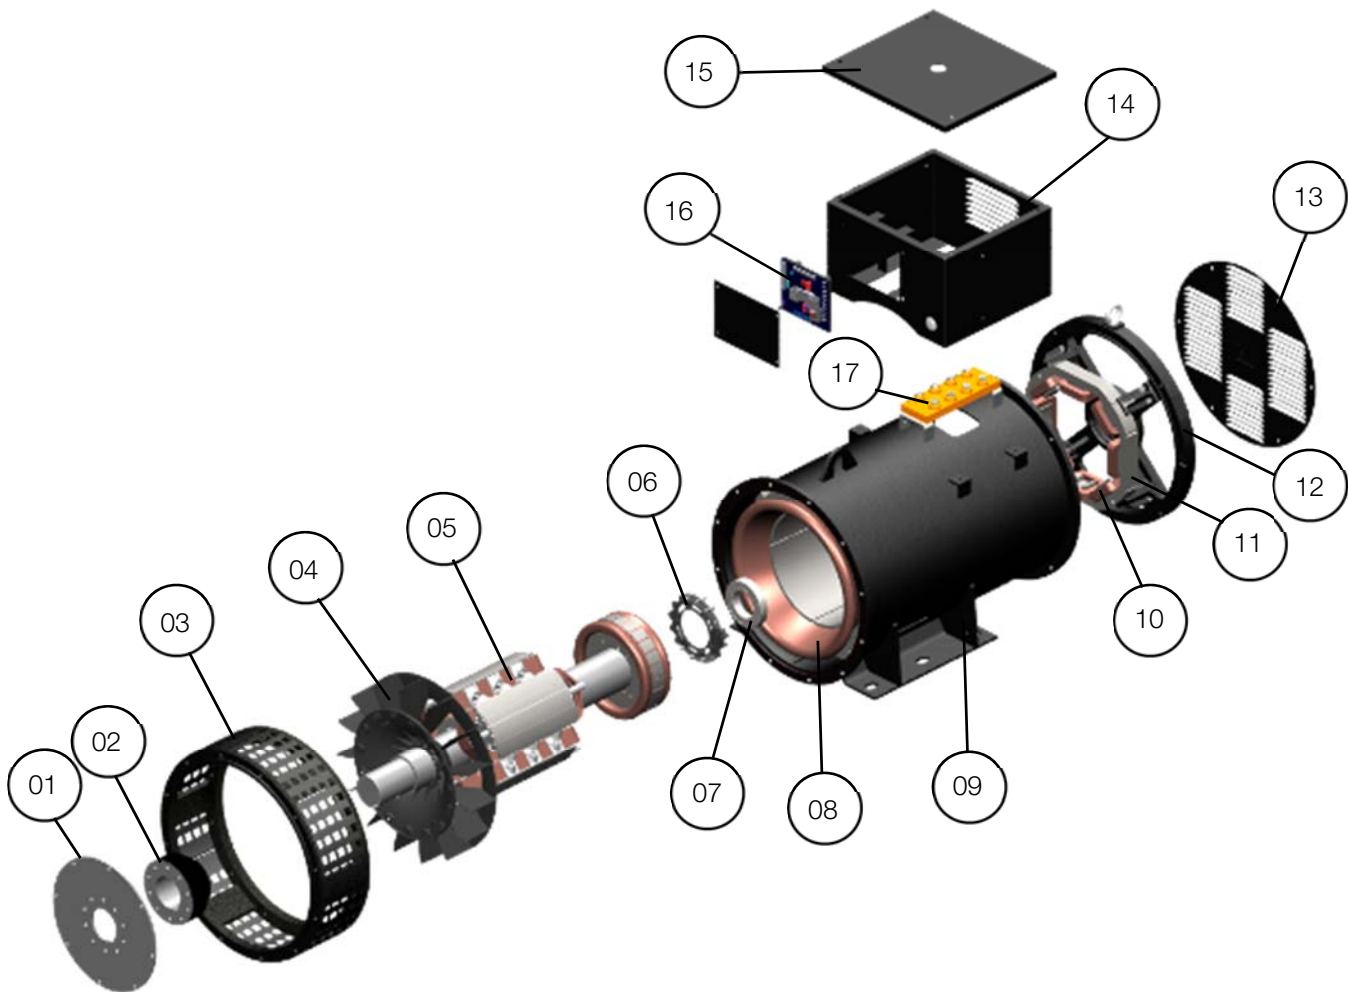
Partes integrantes do gerador WEG Linha G (modelo GTA250)
